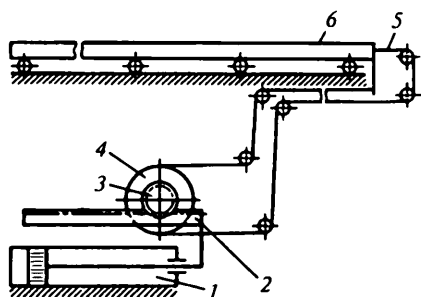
Схема привода транспортирующего стола установок для механопневмоформования
